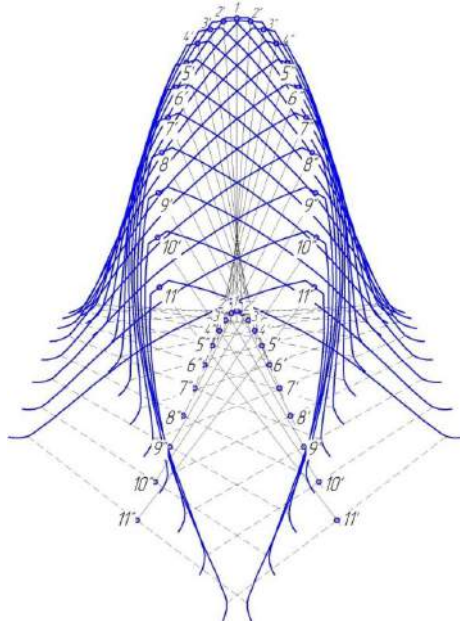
Схема срезания припуска при формировании профиля винтовой поверхности глобоидного червяка ротационным точением многолезвийным инструментом: 11'-11'...2'-2' положение профиля режущего элемента инструмента при входе, 1-1 верхнее положение профиля режущего элемента, 2''-2''...11''-11'' положение режущего элемента инструмента при выходе из впадины профиля глобоидного червяка
